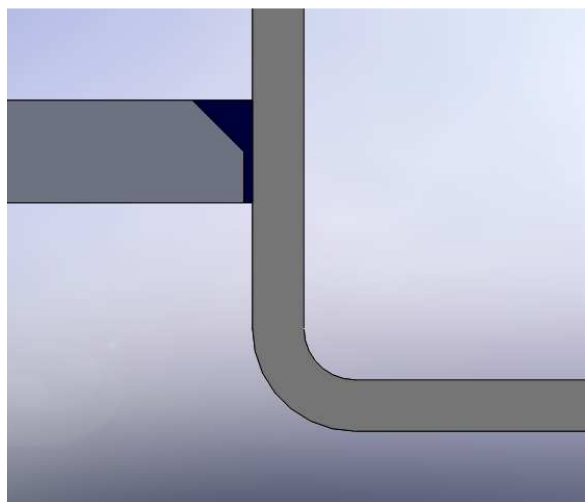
Pormenor do chanfro na placa para melhorar a penetração da soldadura
